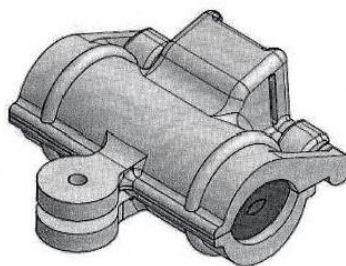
Herraje de Paso o Suspensión. Fuente [22]
